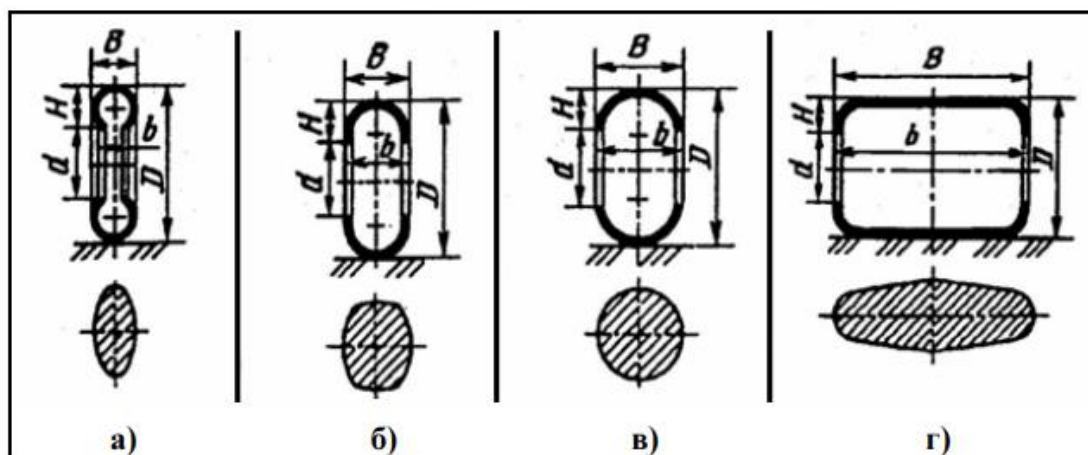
Геометрические формы профиля шин и их отпечатки: а – обычного профиля (тороидная); б – широкопрофильная; в – арочная; г – пневмокоток; D – наружный диаметр шины; B – ширина профиля шины; H – высота профиля шины; d – посадочный диаметр обода колеса; b – ширина обода колеса
